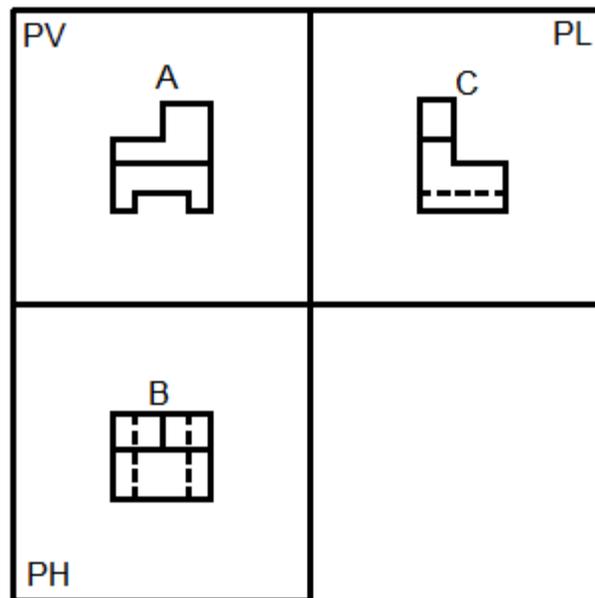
Representación ortogonal de las tres vistas principales en los planos de proyección.
